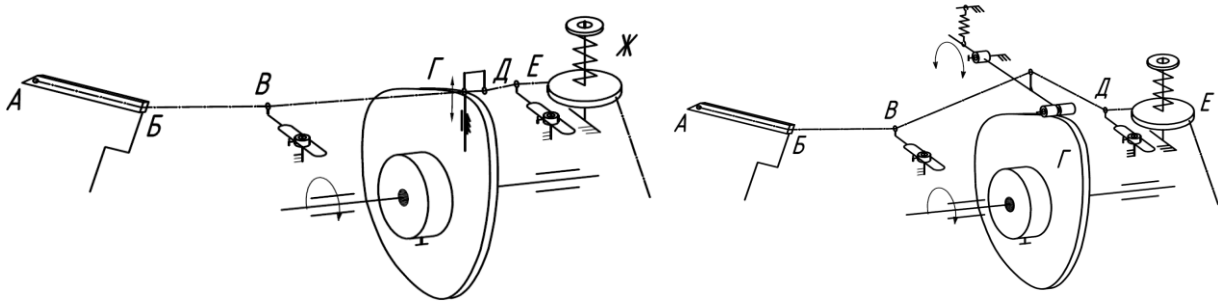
Кінематичні схеми механізмів подачі нижньої нитки швейних машин двохниткового та багато ниткових ланцюгових стібків: а) – кулачково-повзунний; б) – кулачково-коромисловий
